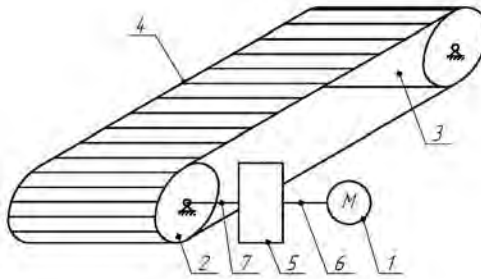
Привод конвейера дискретного действия: 1 – двигатель; 2 – ведущий шкив; 3 – ведомый шкив; 4 – конвейерная лента; 5 – планетарный механизм прерывистого движения; 6, 7 – входной и выходной валы механизма
